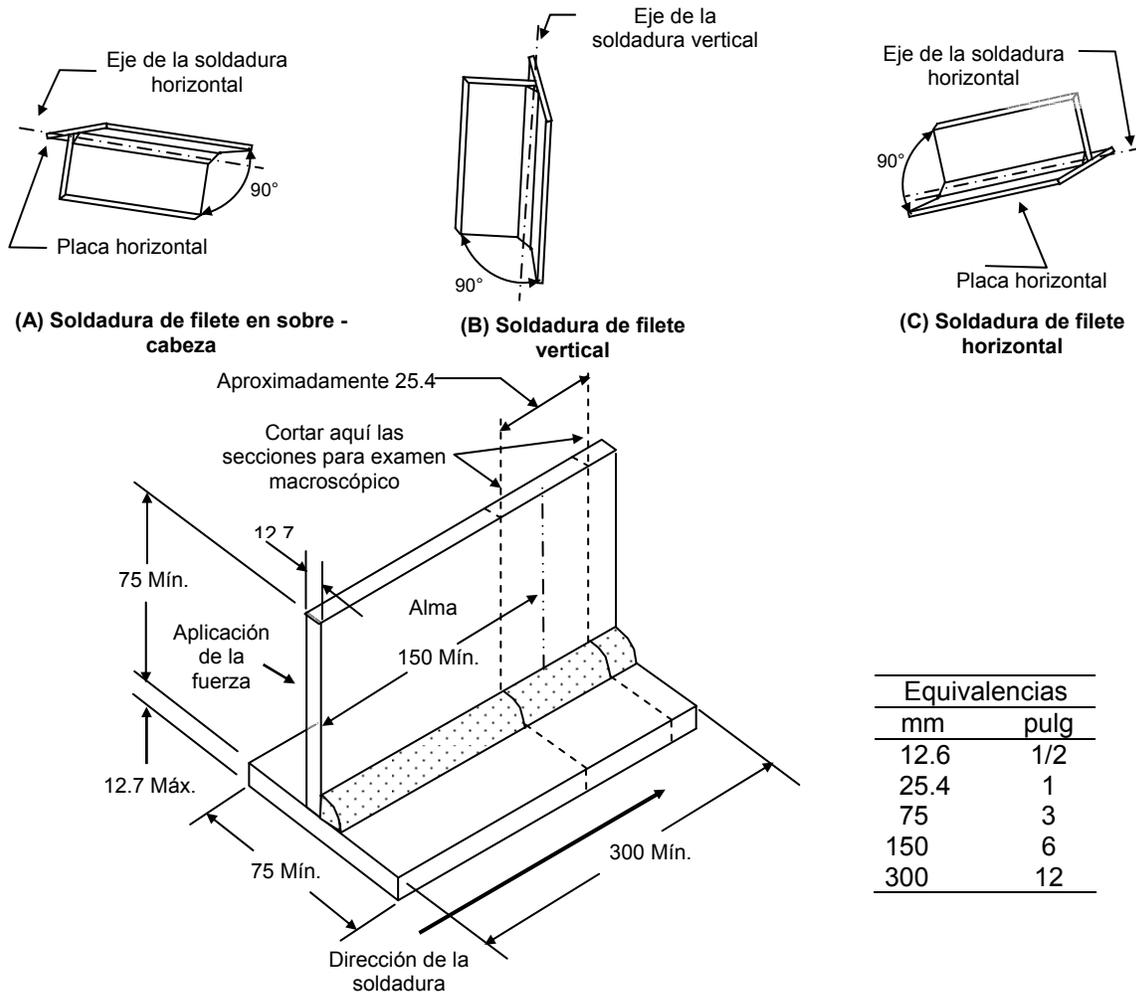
PROBETA PARA LA SOLDADURA DE FILETE
